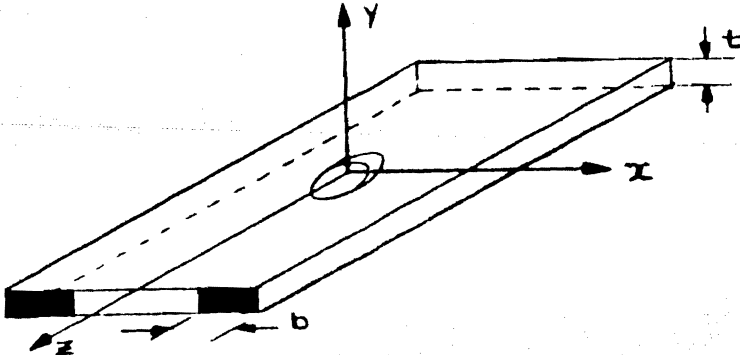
Deducción de las dimensiones de la placa extractora.
